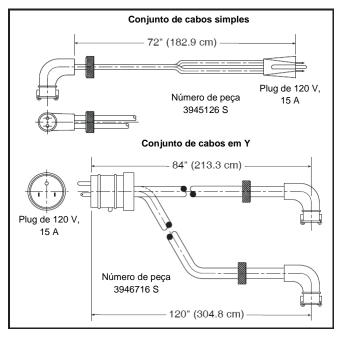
Conjuntos de cabos do aquecedor elétrico
